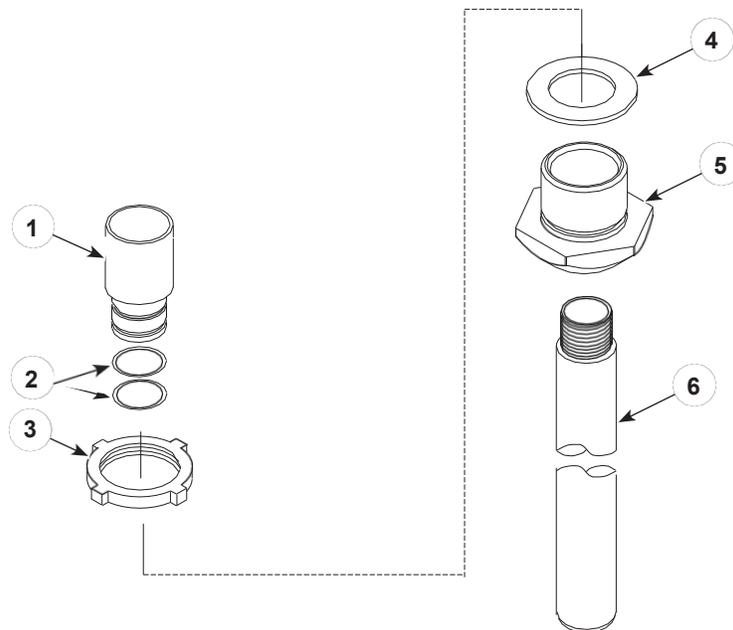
NHR-8-25 und NHR-8-80 Aufnahmerohr und Pumpenadapter
